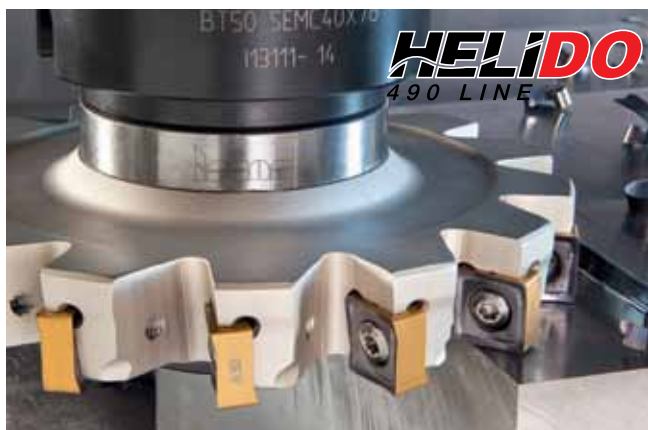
Фреза HELIDO 890 с двусторонними пластинами, закрепляемыми радиально
